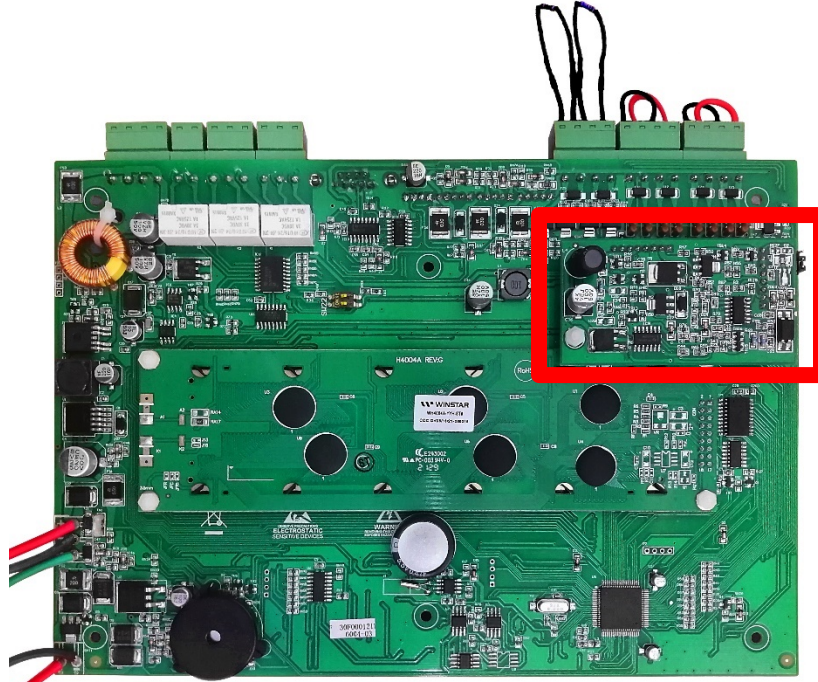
Main board con tarjeta de expansión de 1 lazo instalada
